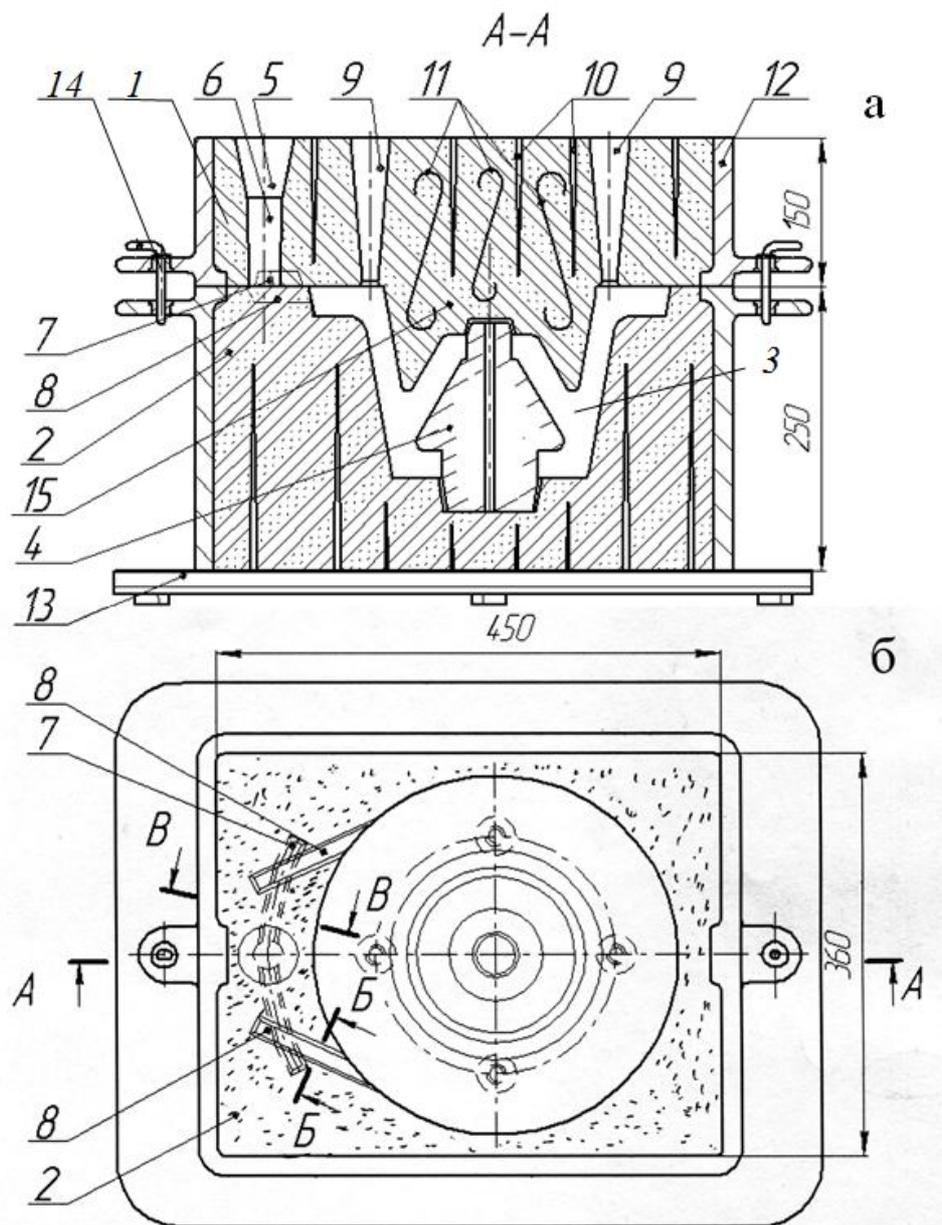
Собранная литейная форма: а – форма в разрезе (А-А), б – вид сверху нижней полуформы при снятой верхней полуформе; 1 – верхняя полуформа, 2 – нижняя полуформа, 3 – полость формы, 4 – стержень, 5 – литниковая воронка, 6 – стояк, 7 – шлакоуловитель, 8 – питатели, 9 – выпор, 10 – наколы, 11 – крючки; 12 – опока, 13 – подопочная плита, 14 – штырь центрирующий, 15 – «болван»
